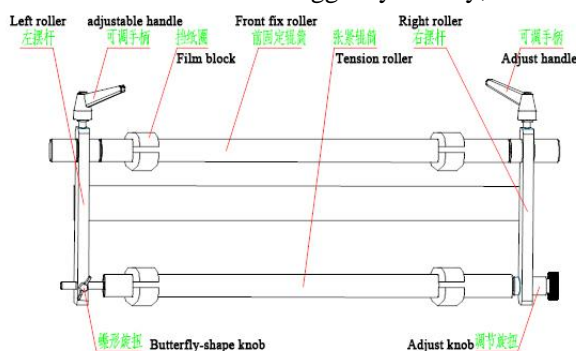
前摆杆机构示意图 FIG. 29 schematic diagram of front swing rod mechanism
